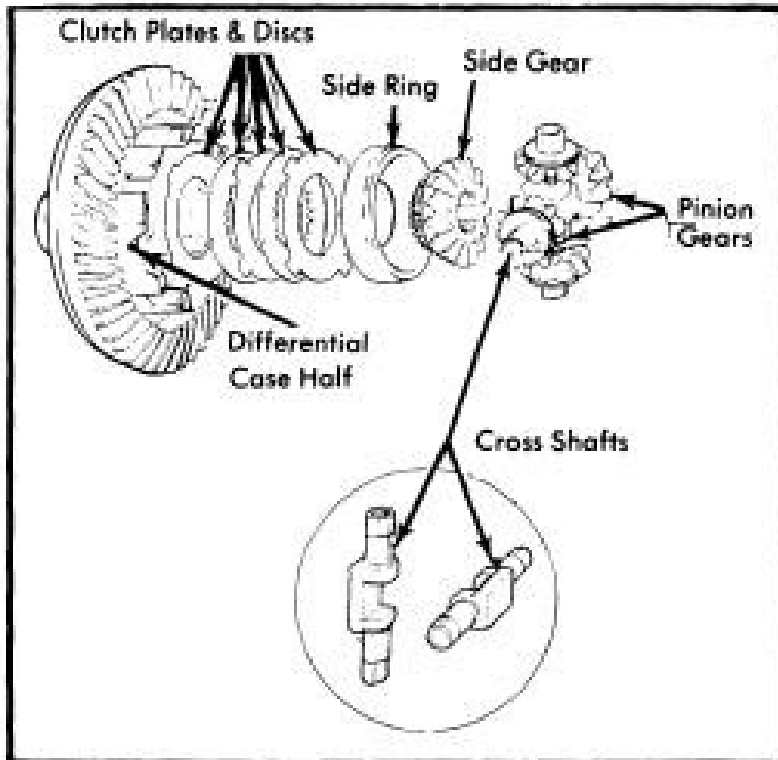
Explosionszeichnung des begrenzten Schlupfes
